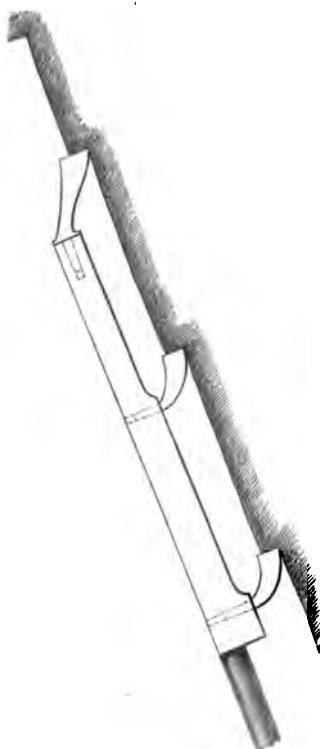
Werkzeug der Maschine von Carret, Marshall & Co.
